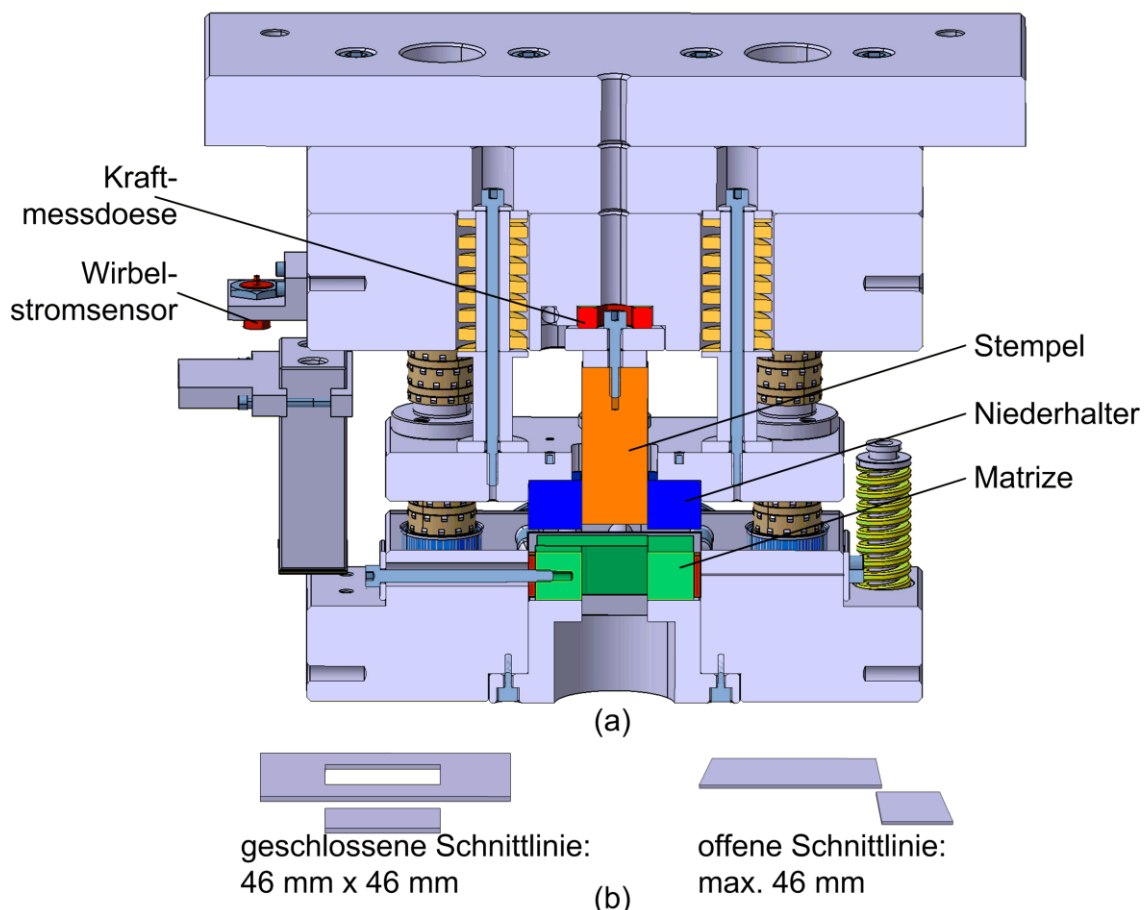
Versuchswerkzeug zum Hartschneiden (a) und Versuchsgeometrien (b)
